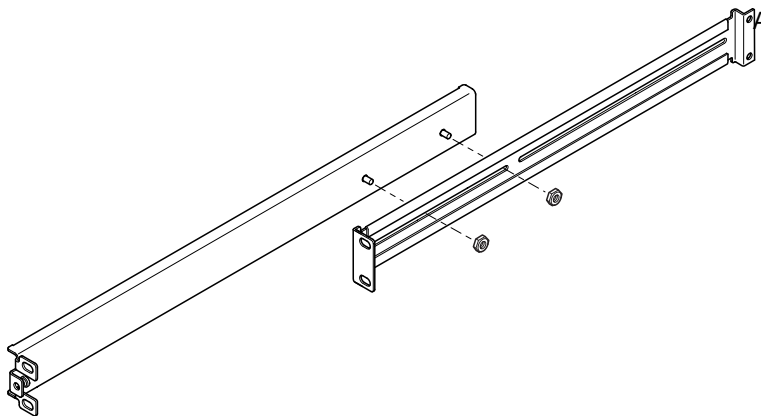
Placement des supports guidés pour un châssis Sun StorEdge de 72 pouces de hauteur
